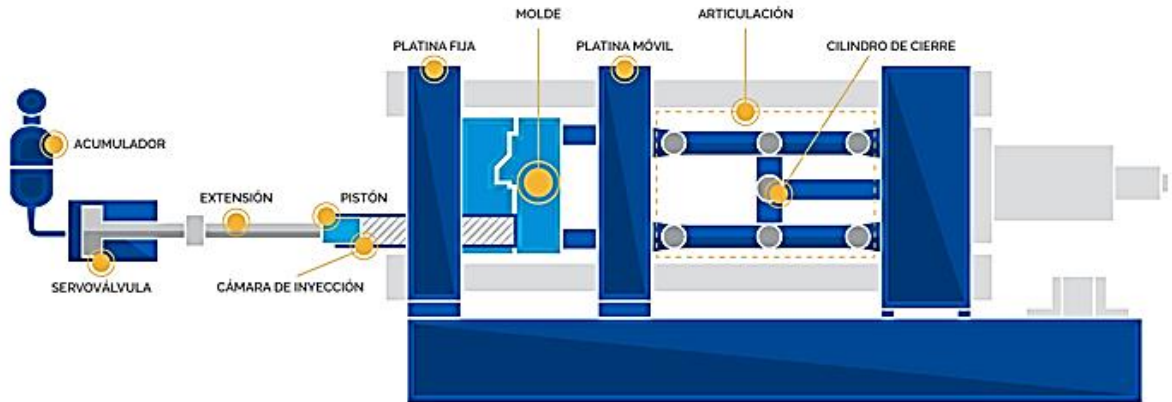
componentes de una máquina de fundición a presión en cámara fría
